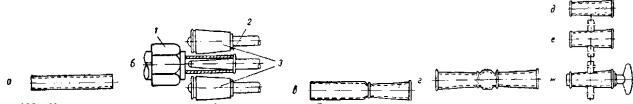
Изготовление стеклянных муфт для кранов на обкаточном станке: а—заготовка на две муфты; б—узел для изготовления муфт механизированным способом (1 — патрон специального приспособления; 2—керн, вводимый в обогреваемую горелкой трубку; 3—ролики, прижимающие к керну заготовку); в—заготовка муфты с готовым рантом; г—заготовка с двумя муфтами и последующим отжигом; д—муфта после удаления лишнего стекла; е — муфта с припаянными к ней отводными трубками; ж—готовый край-
